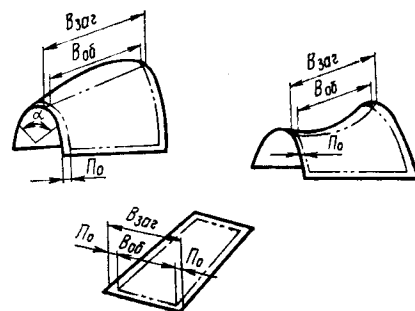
Схема определения ширины заготовок обшивок двойной кривизны, изготавливаемых обтяжкой.
